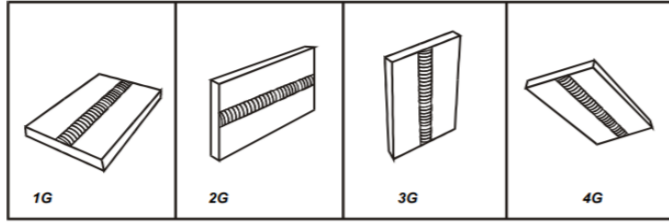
Diferentes vistas de una soldadura a tope [44].
